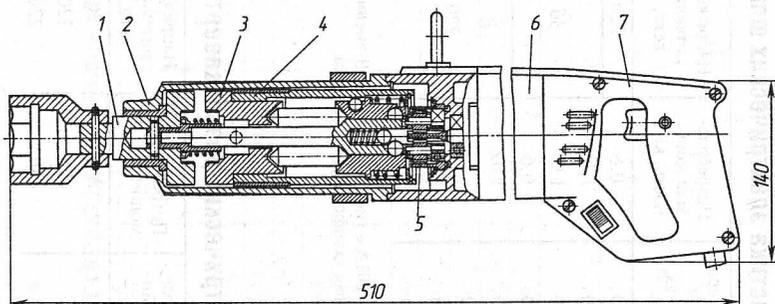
Рис. к приложению 53. Гайковерт ИЭ-3119: 1 — шпindelь; 2 — корпус; 3 — ударно-вращательный механизм; 4 — корпус бойка; 5 — планетарный редуктор; 6 — электродвигатель; 7 — рукоятка
